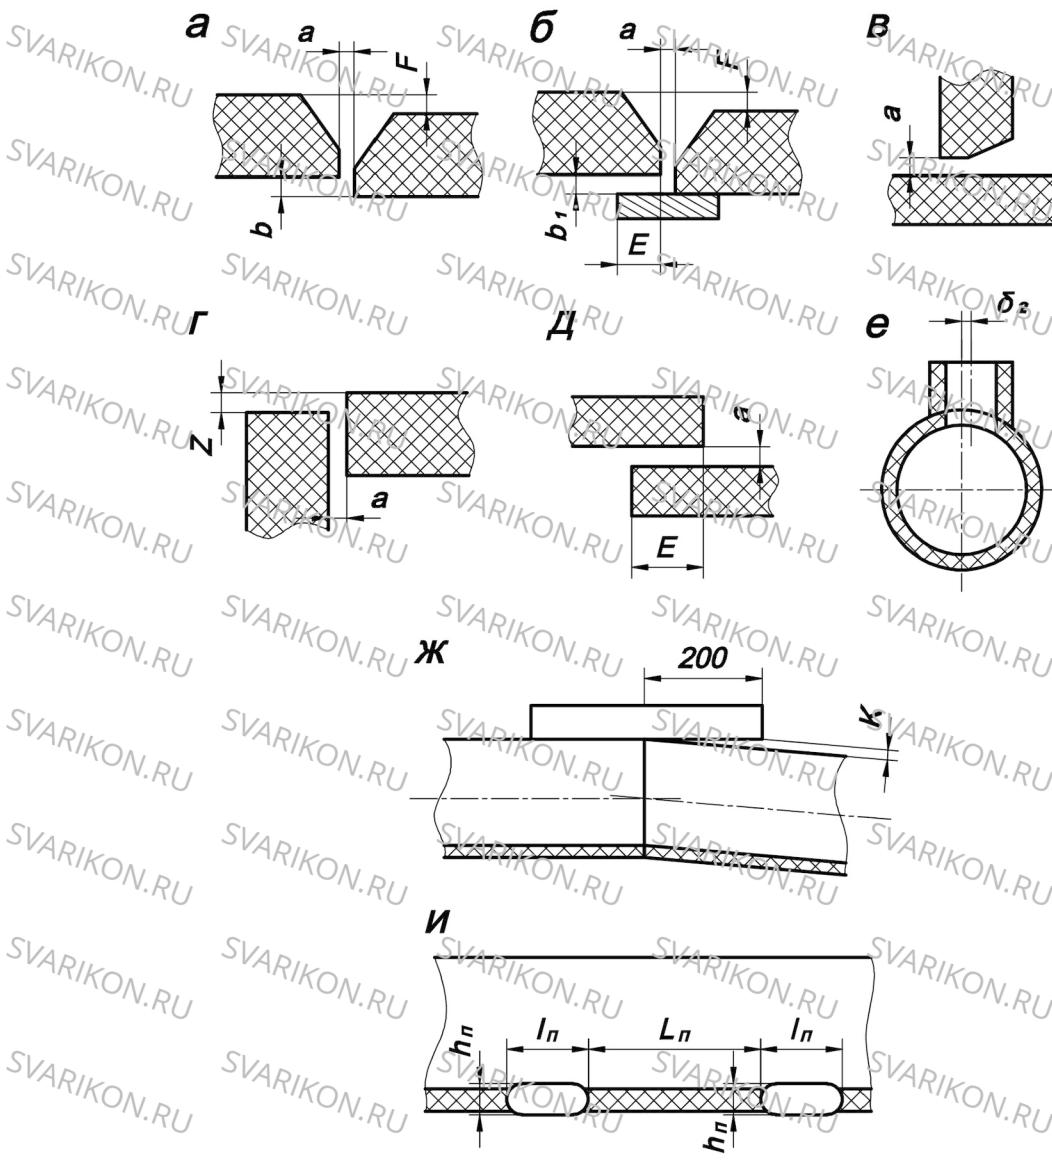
Размеры, контролируемые измерением при подготовке деталей под сварку:
